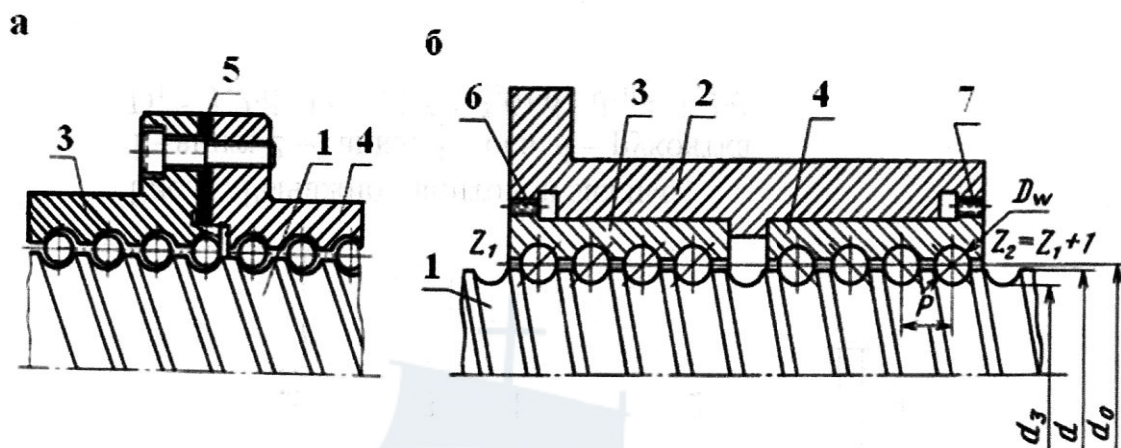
Конструкция ШВП с регулируемым натягом:
